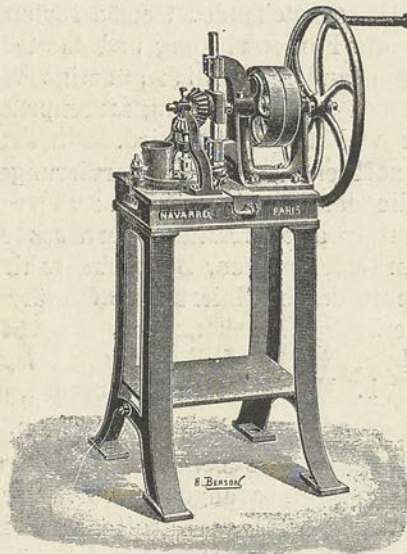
Formenschneidemaschine für Leipziger Allerlei.
